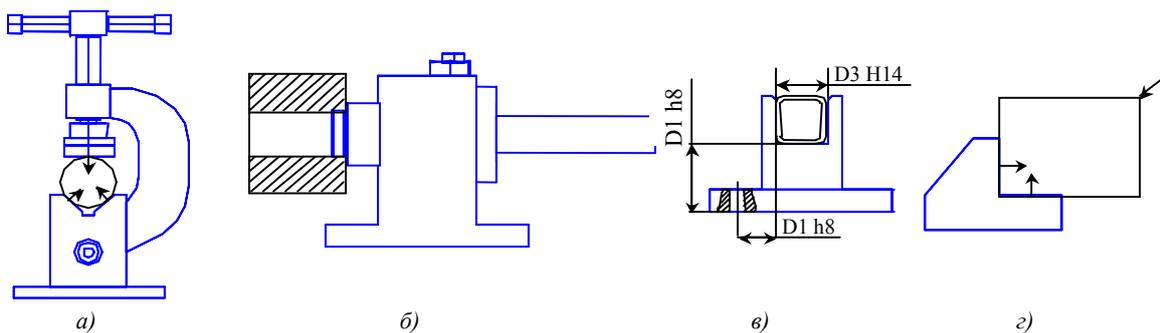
Примеры комбинированных конструктивных элементов: а) струбцина; б) палец выдвижной; в) вилка установочная; г) упор комбинированный
